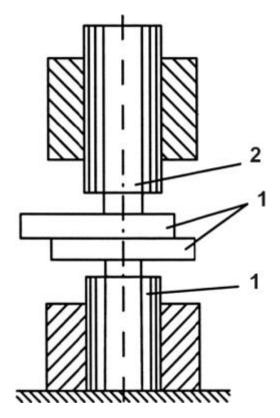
Схема холодной сварки без предварительного зажатия свариваемых деталей: 1 — свариваемые детали; 2 — пуансоны.
